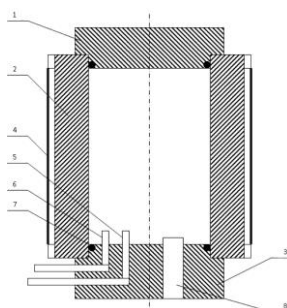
Схематическое изображение сосуда высокого давления: 1 - верхняя заглушка СВД; 2 - корпус СВД; 3 - нижняя заглушка СВД; 4 - рубашка охлаждения; 5 - токоввод донного нагревателя; 6 - токоввод бокового нагревателя; 7 - кольцевое полимерное уплотнение; 8 - вакуумный клапан.
